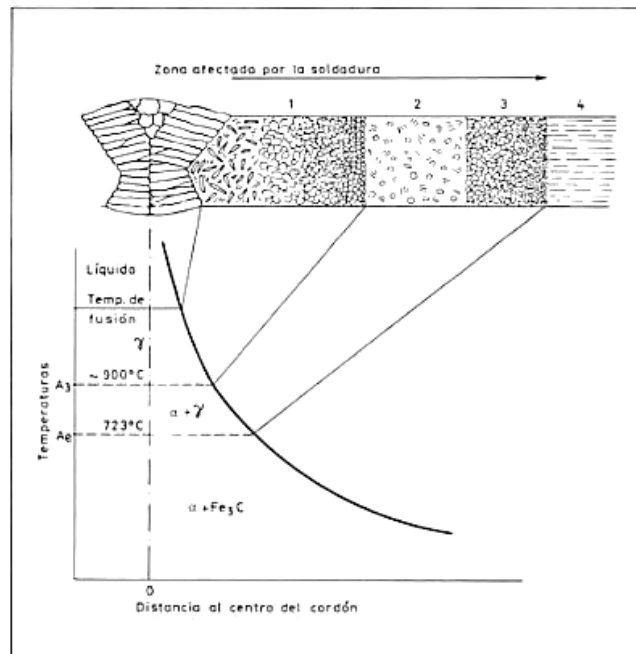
Esquema de las zonas existentes en la soldadura por fusión.
